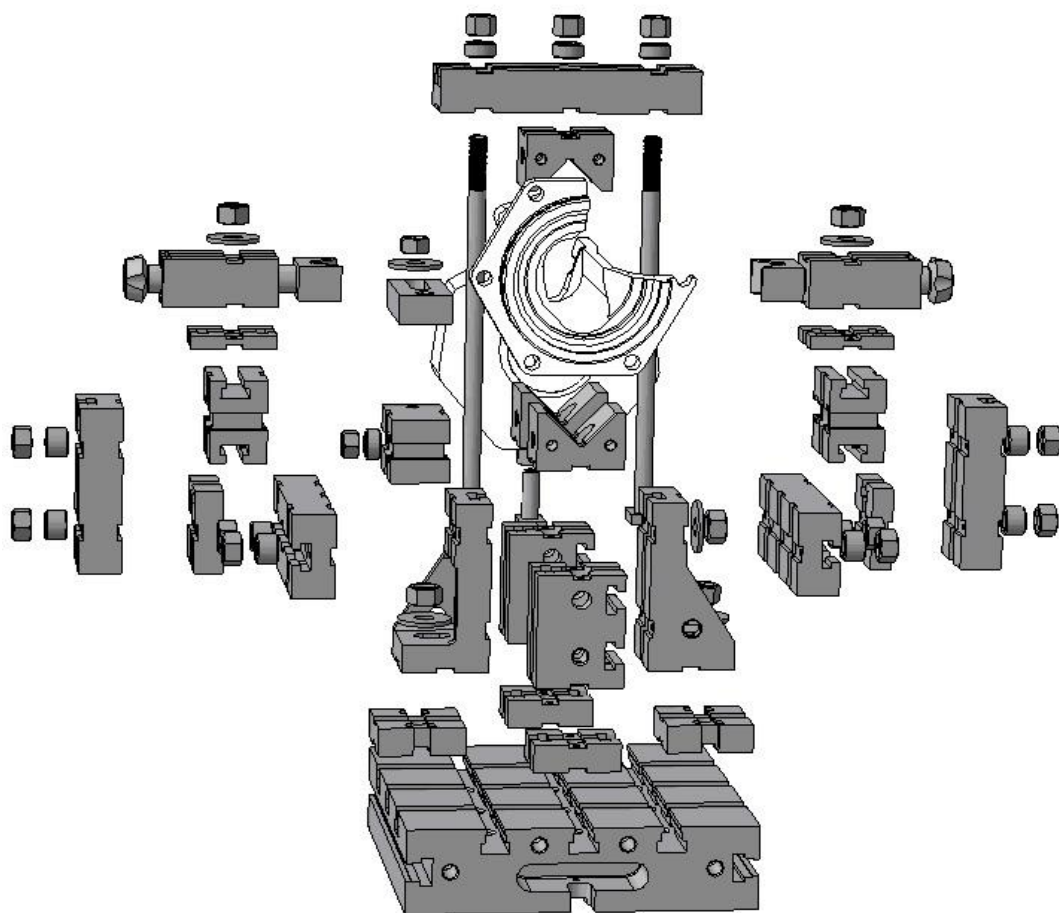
Ассоциативные схемы сборки и контурное изображение универсально-сборного приспособления
